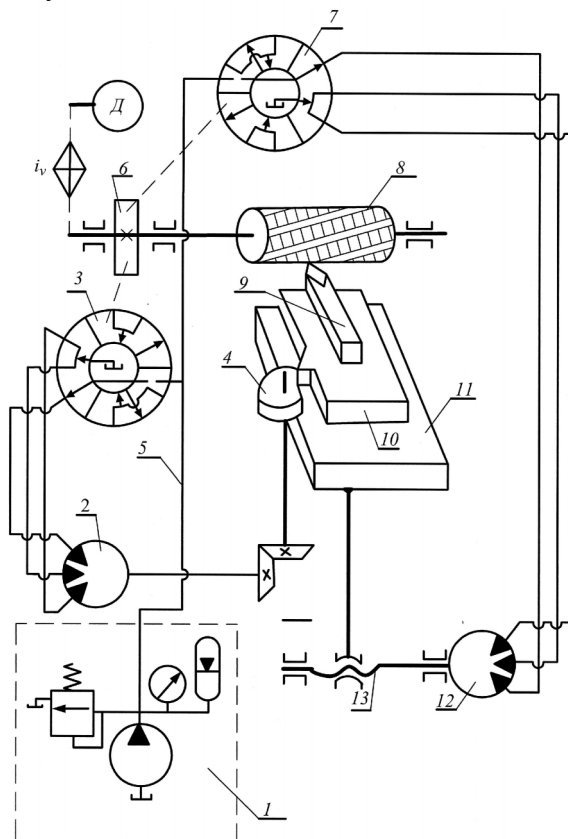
Структурная схема токарно-затыловочного станка с гидравлическими формообразующими связями для затылования фрез
